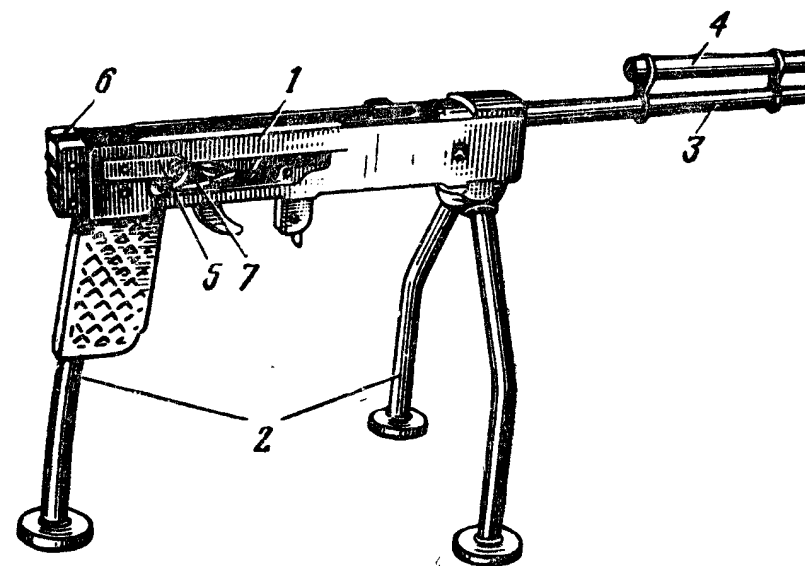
Станок для показа работы частей и механизмов автомата (ручного пулемета) Калашникова:
